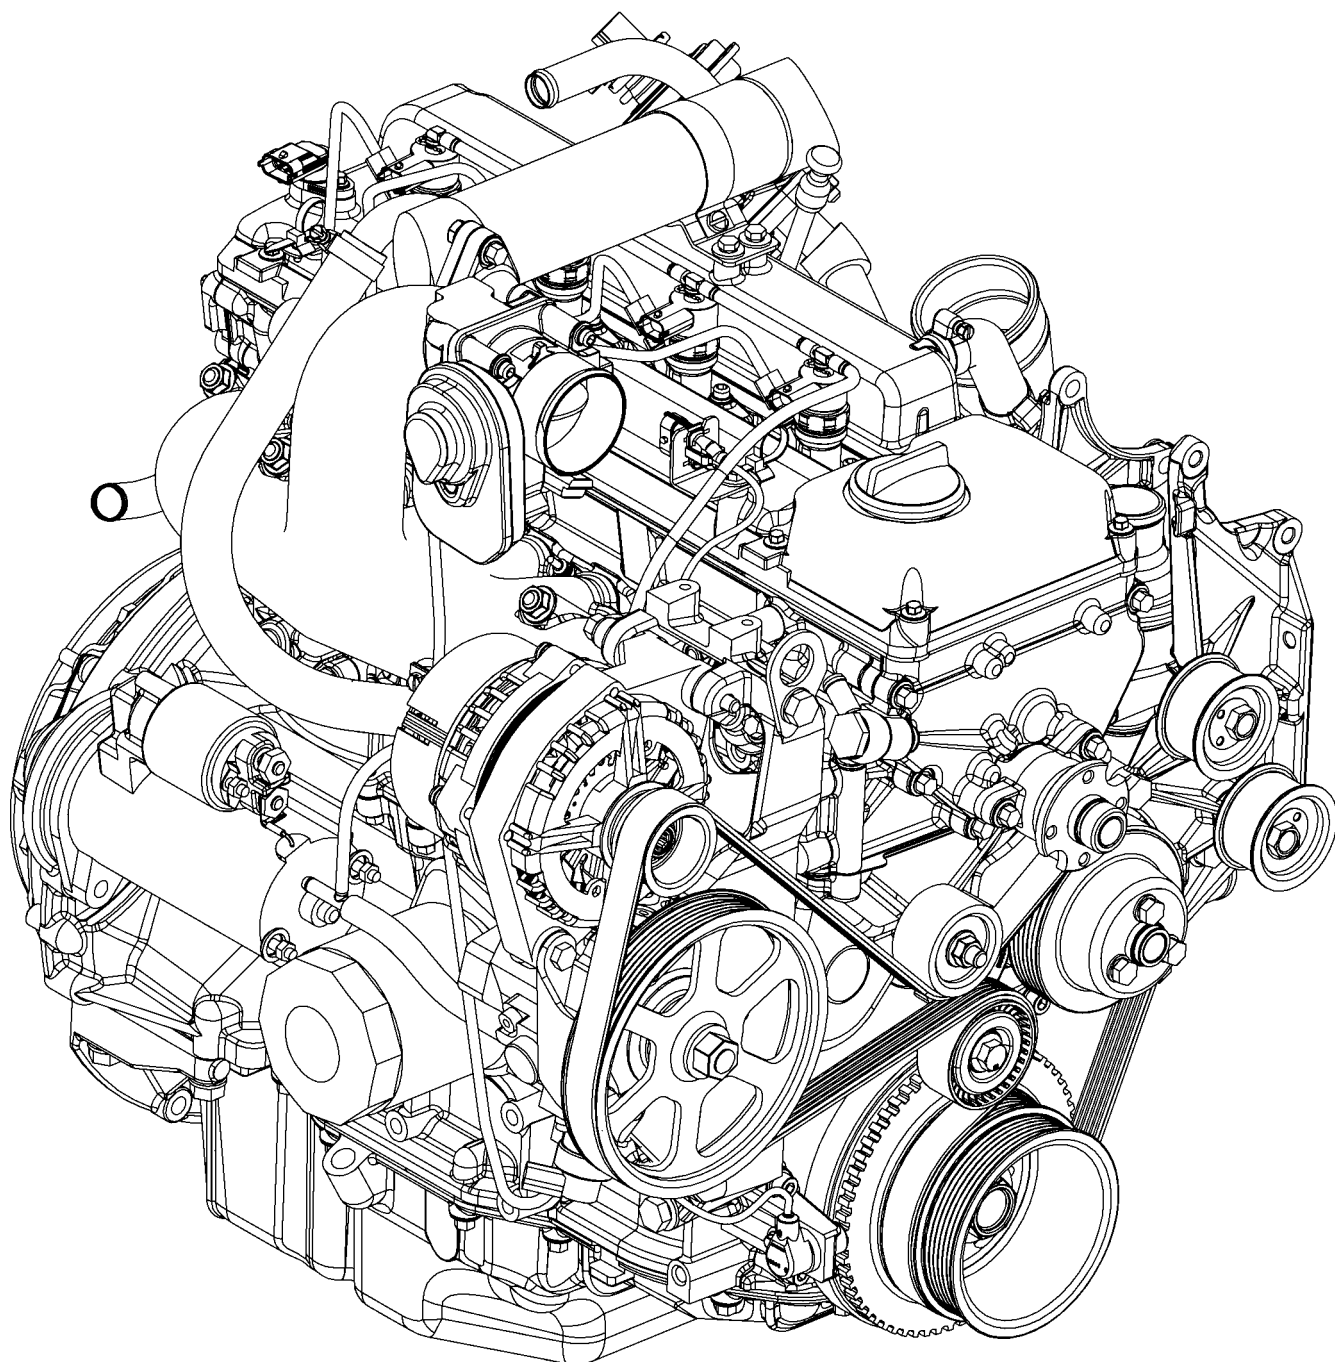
в. Внешний вид двигателя без компрессора кондиционера, насоса ГУР и деталей привода вентилятора
